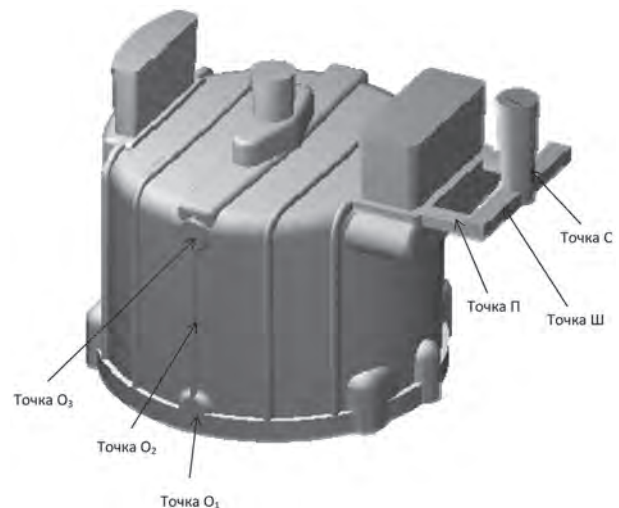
Вариант с суживающейся литниковой системой отливки «Корпус»
